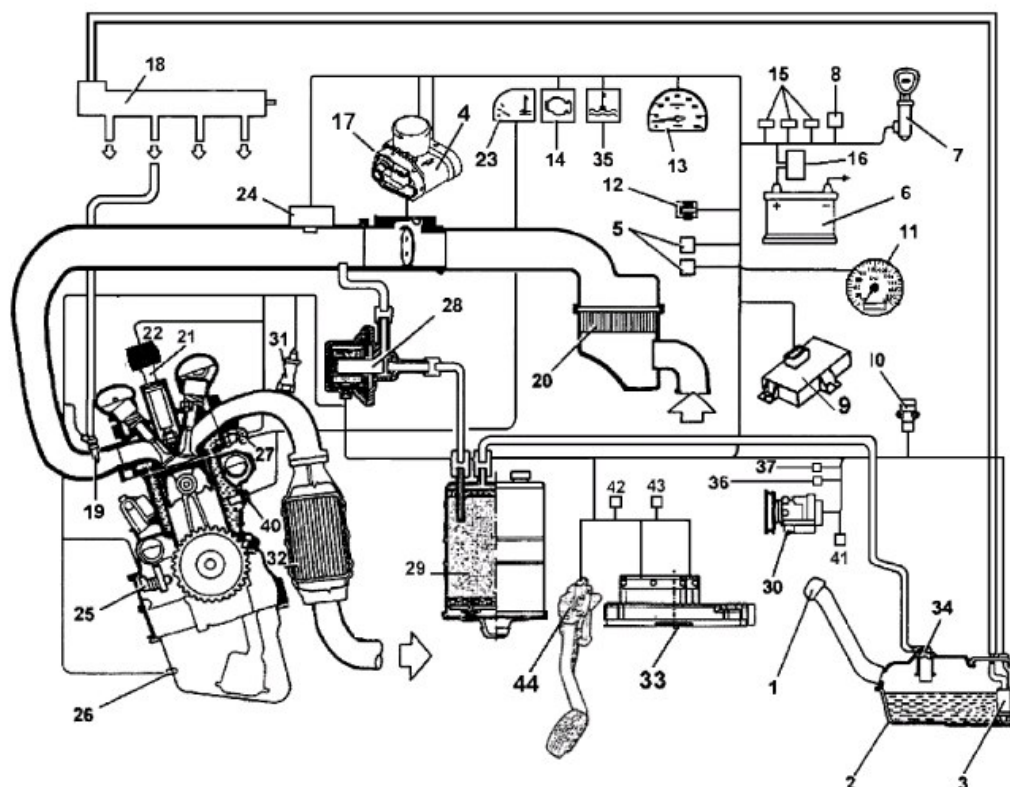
Vista de conjunto de gerenciamento de motor IAW 5NF
